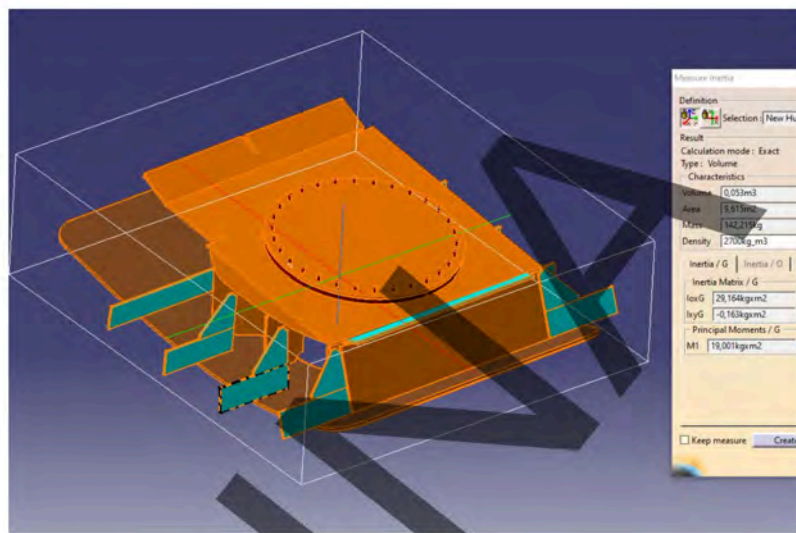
Diseño cofferdam (Fuente: Trabajo de campo)
